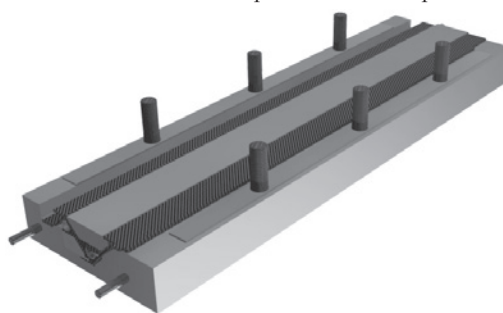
Приспособление для сборки и склеивания лопаток сепаратора в открытом виде (в приспособлении выставлены детали лопатки сепаратора)
